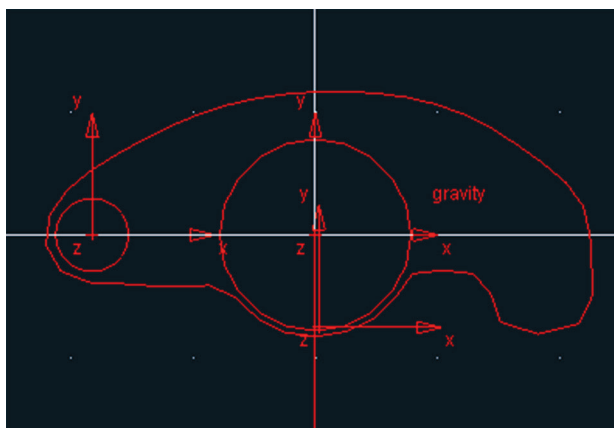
(b) – Círculo construído na origem (0,0,0).
